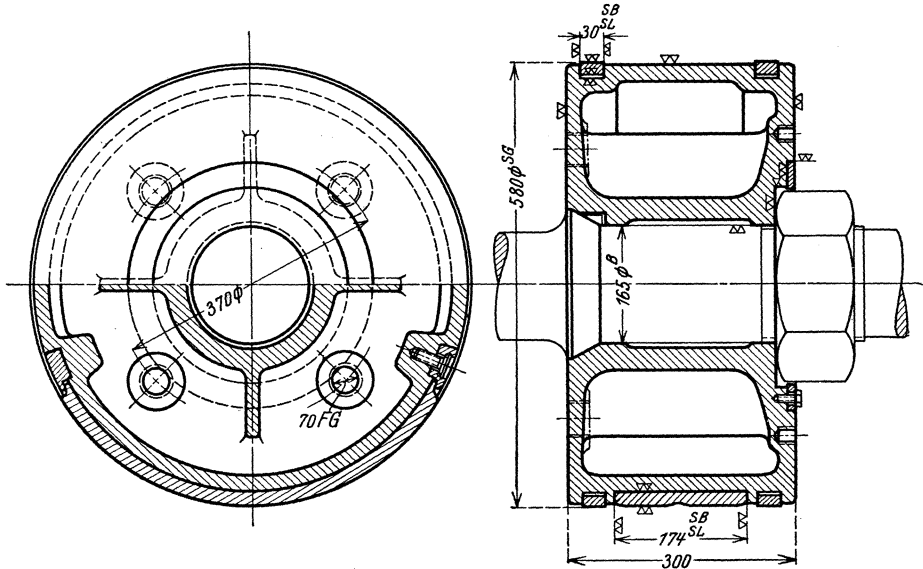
Hochdruck-Dampfmaschinenkolben. (A. Borsig G. m. b. H., Berlin.)
